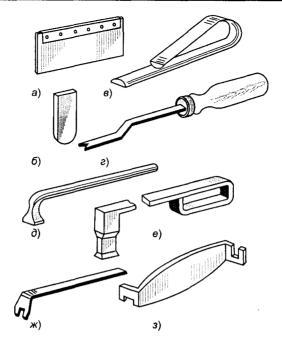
Набор инструмента обмотчика: a — фибровая пластинка; b — фибровый язык; b — обратный клин; b — угловой нож; d — выколотка; d — топорик; d — ключи для гибки роторных стержней
